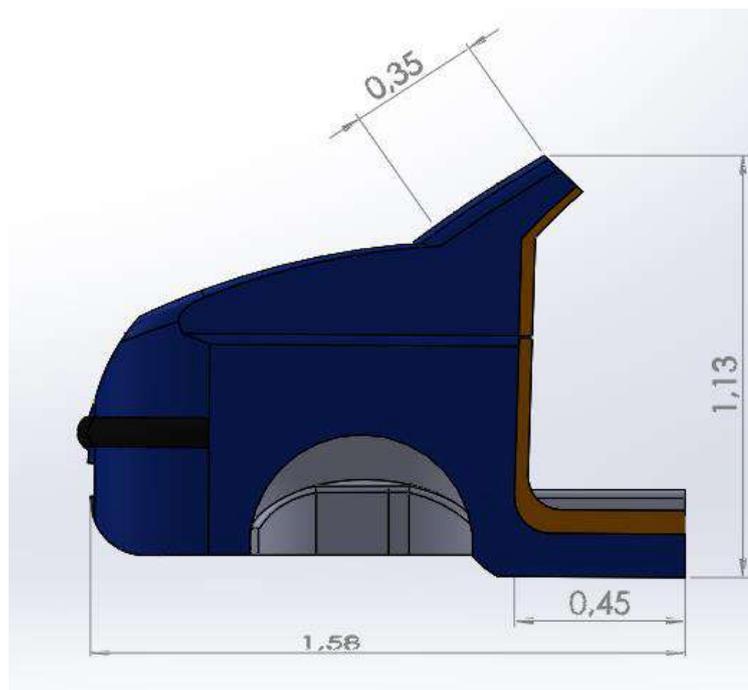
Diseño de los cortes de la carrocería parte delantera vista frontal
